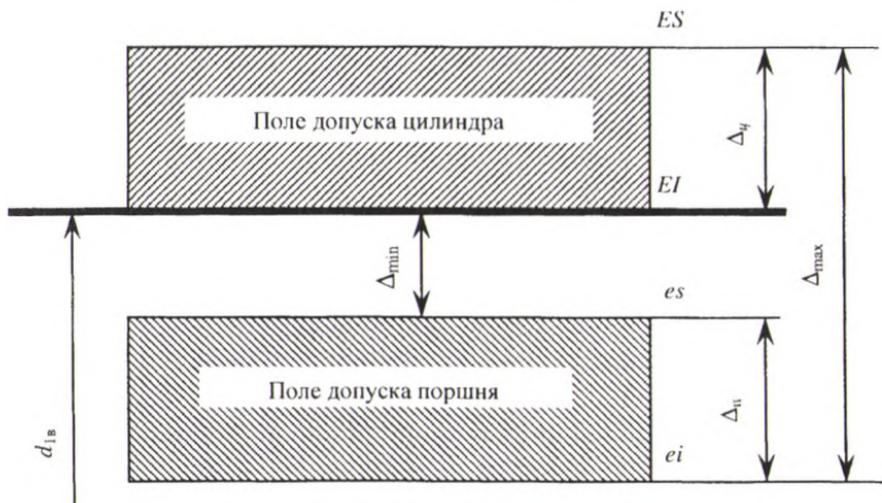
Схема расположения полей допусков поршня и цилиндра гидростойки
